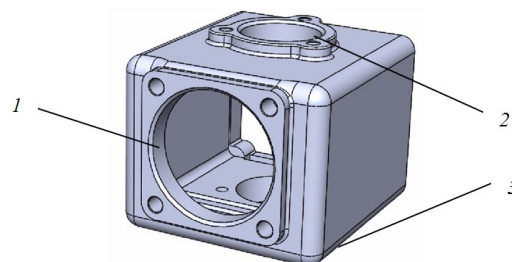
3D-модель деталі «корпус», яка виконана у програмному продукті SOLIDWORKS: 1 - основний отвір; 2 – базовий отвір; 3 – базова площина корпусу
